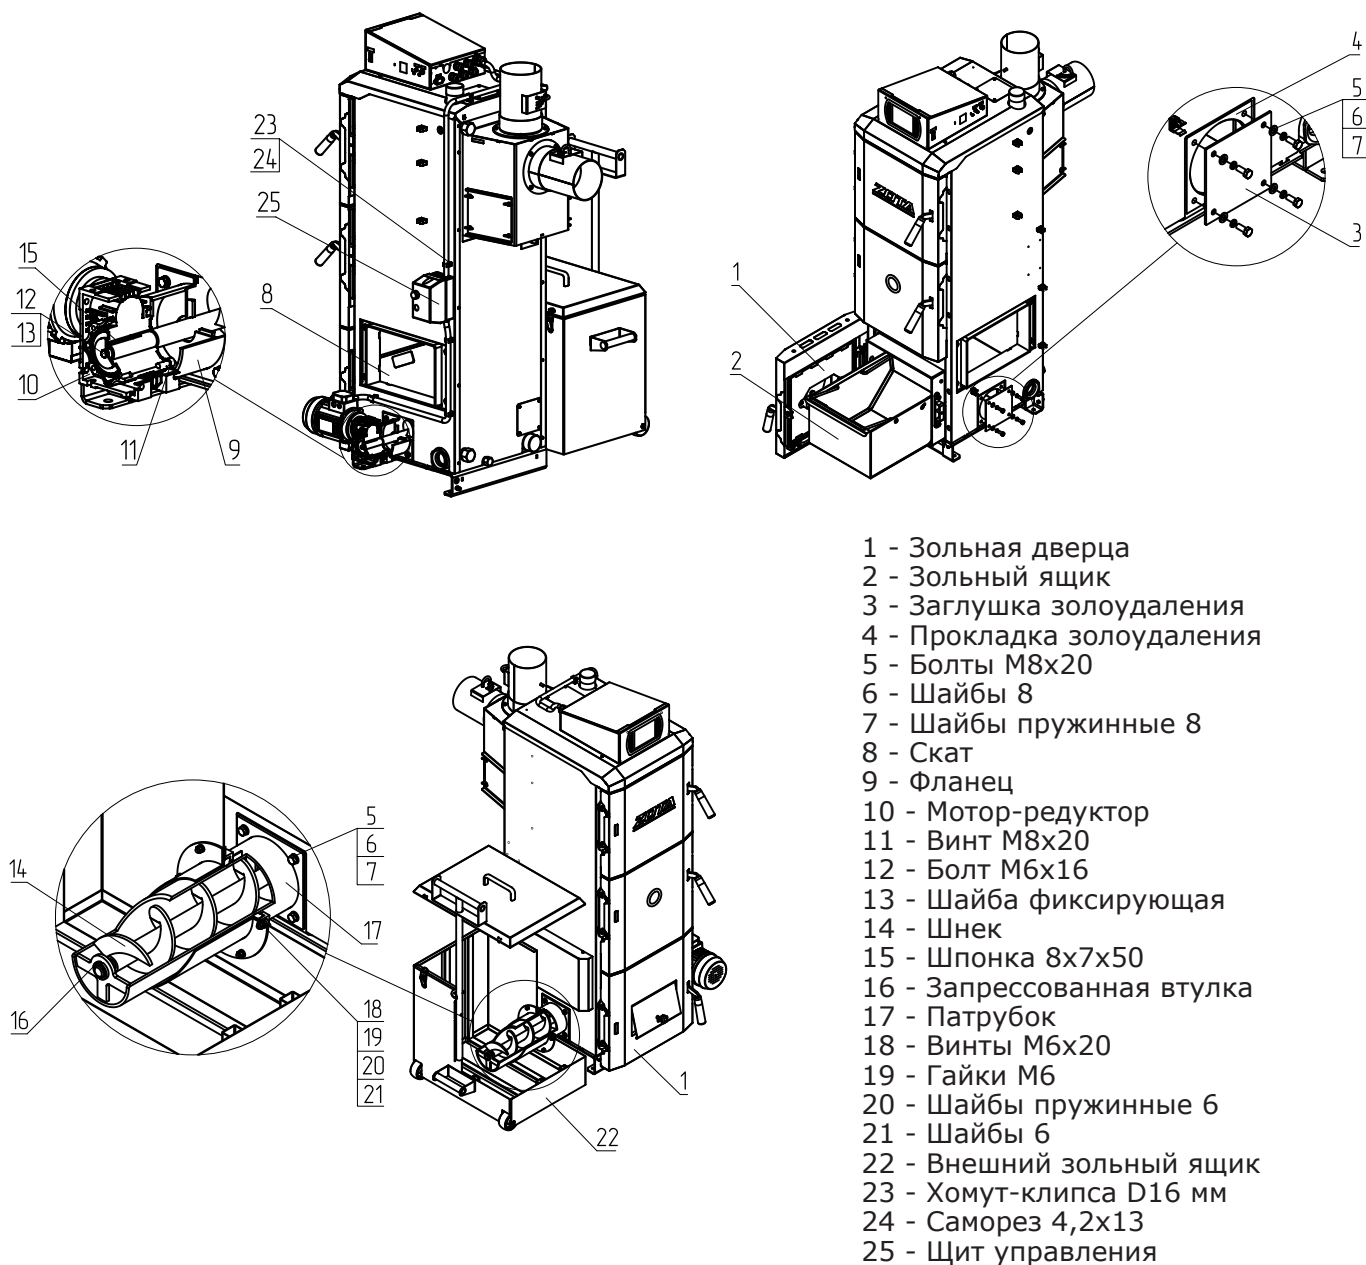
Монтаж золоудаления котла ZOTA Stahanov 16-65 кВт.
